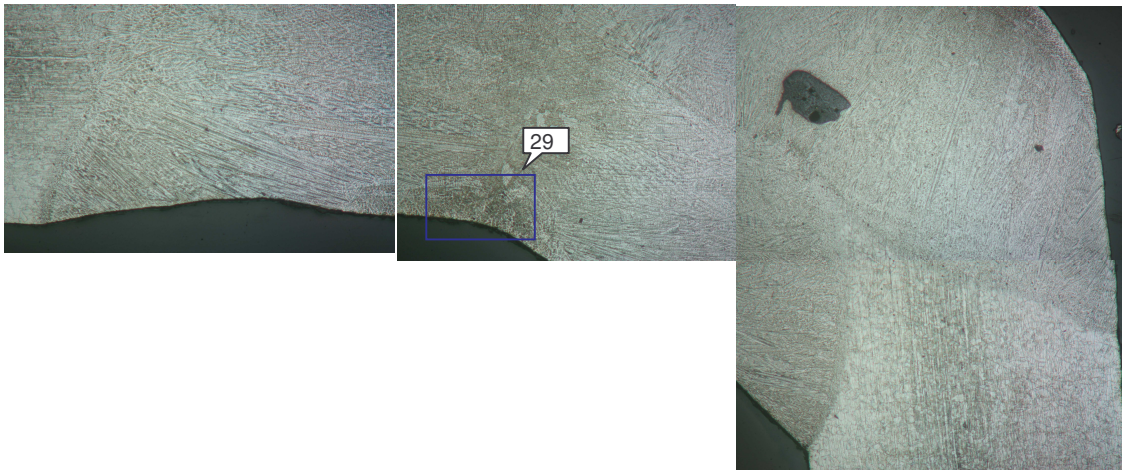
Querschnitt durch die Schweißnaht
